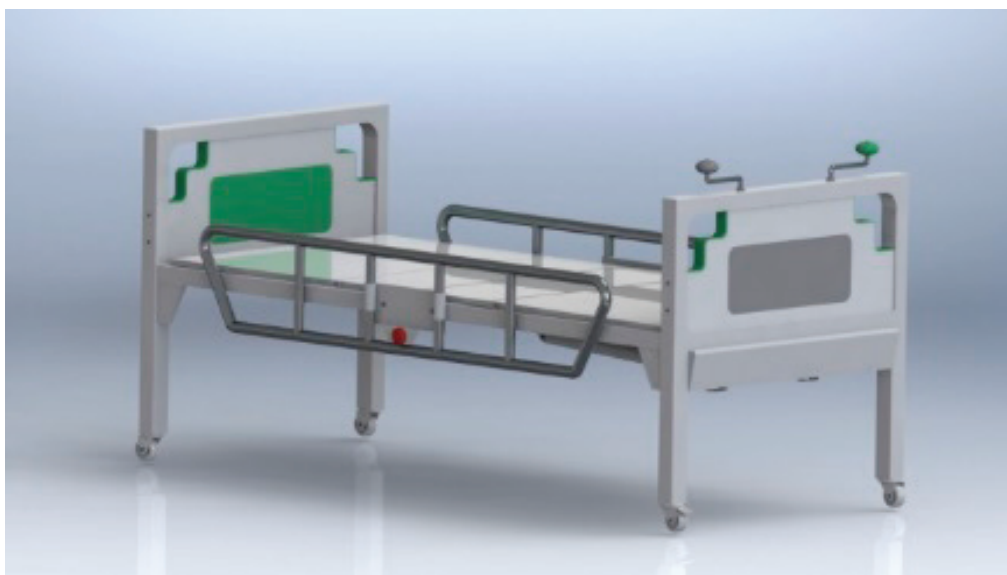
Aspectos estruturais do produto com dimensões gerais.
